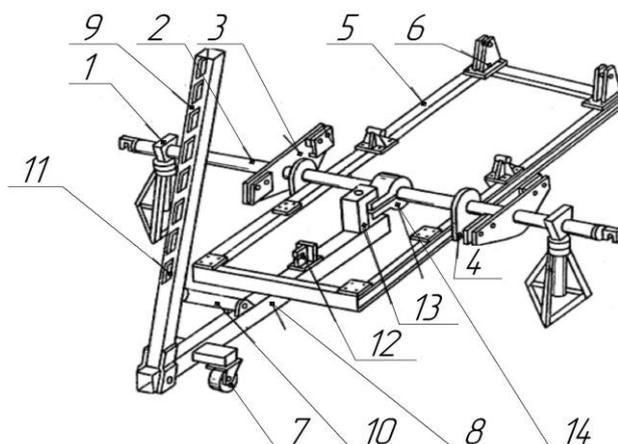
Устройство для правки кузовов авторское свидетельство №14338884: 1-опора; 2-штанга; 3-зажим; 4-направляющие; 5-рама; 6-подставки; 7-колесо; 8-балка; 9-рычаг; 10-гидроцилиндр; 11-гребенка; 12-упор; 13-серьга; 14-кронштейн.
